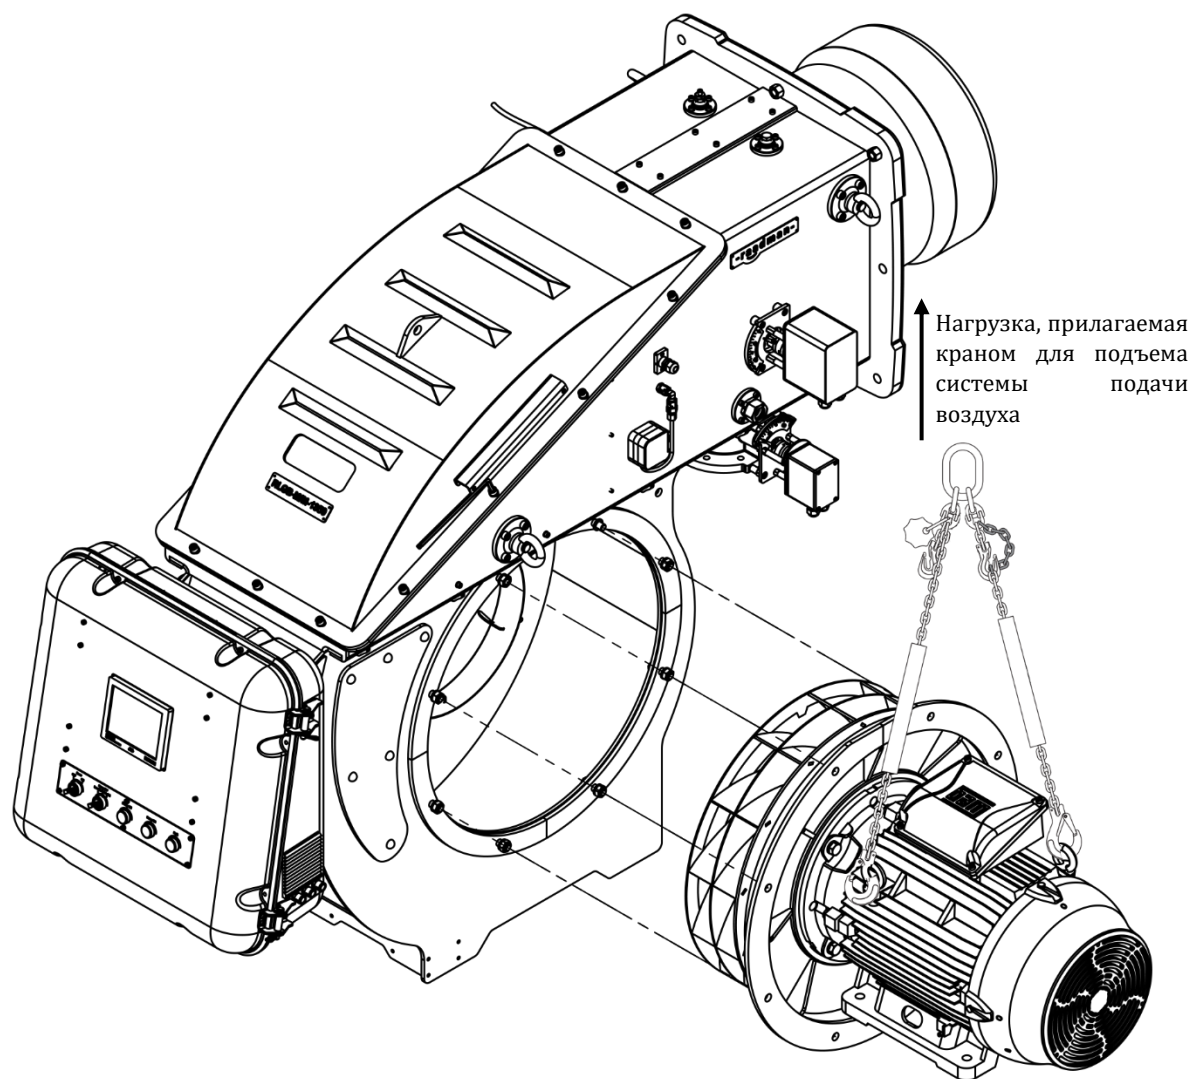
Установление двигателя и вентилятора на корпус горелки RGB-M-1350
